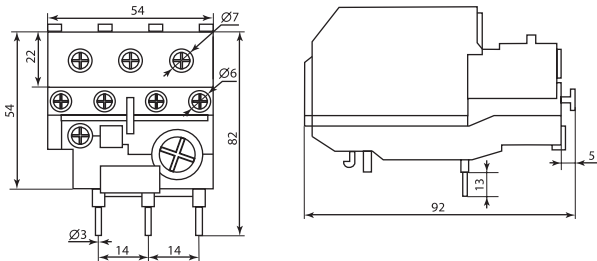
Габаритные и установочные размеры реле РТЛУ-2053-М2
